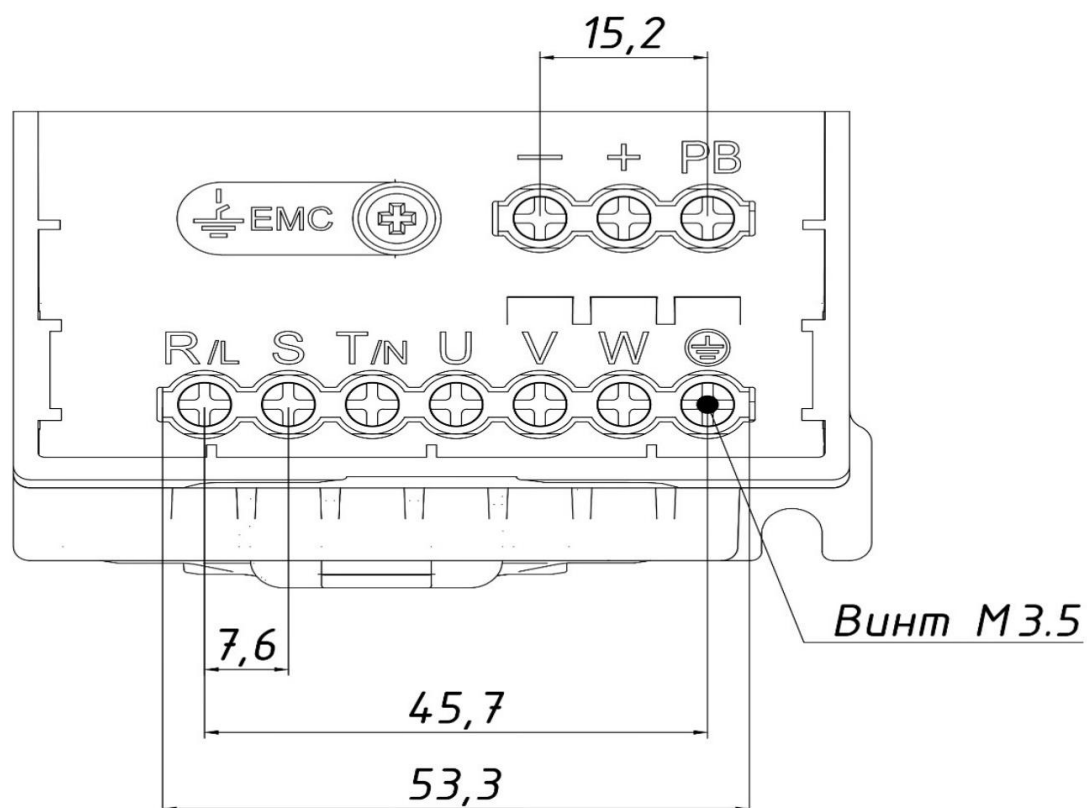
Размеры клемм цепи питания, типоразмер B1
